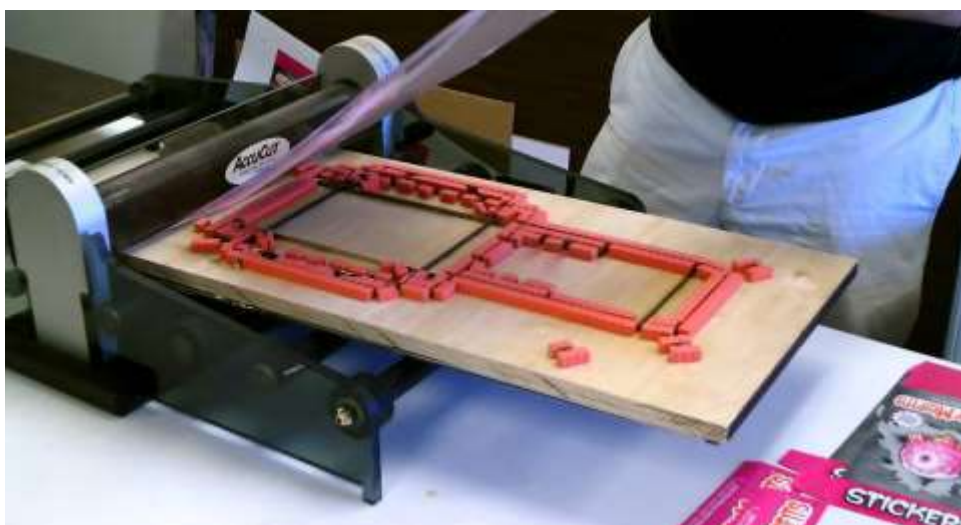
Плоскоциліндричний прес для висікання
